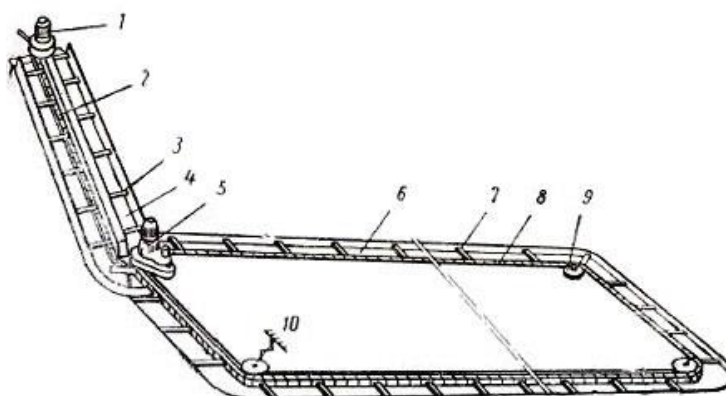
Навозоуборочный скребковый транспортер ТСН-2Б
